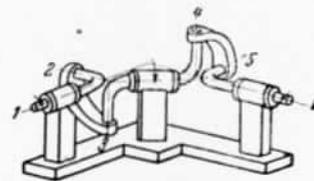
Пространственный шестизвенный шарнирный механизм.
